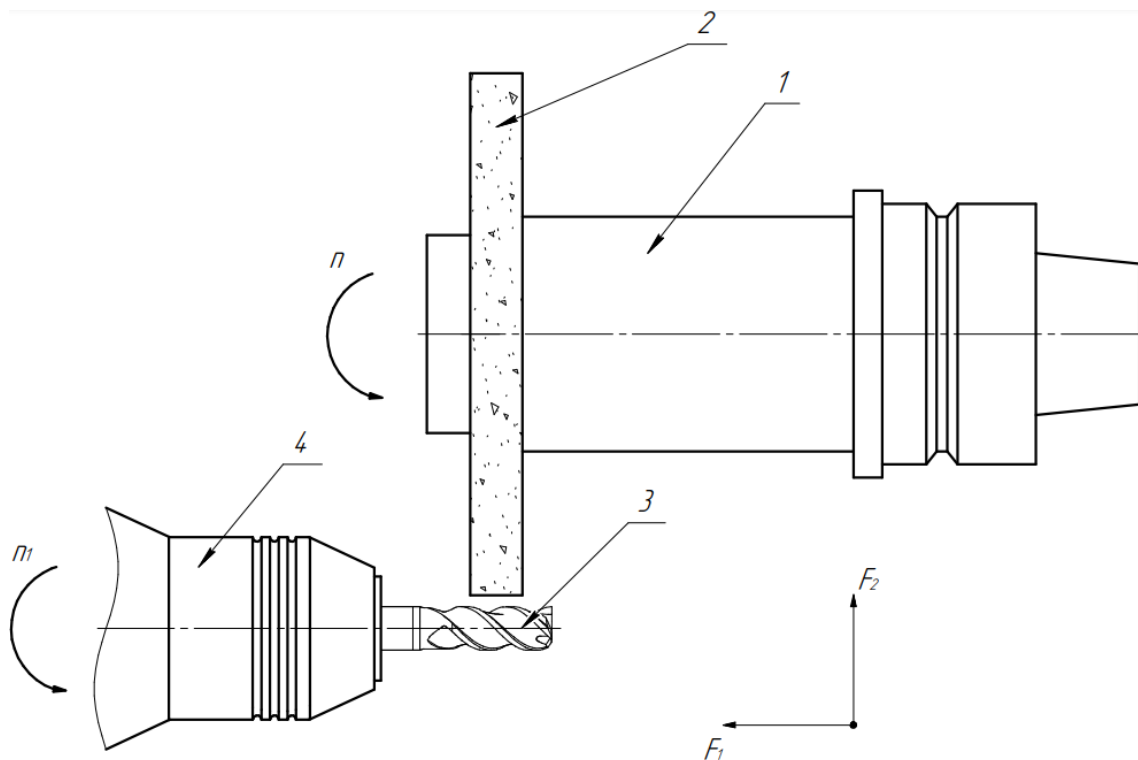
Схема обработки.: 1) шлифовальная оправка; 2) дисковая абразивная щетка; 3) обрабатываемое изделие; 4) инструментальный патрон
